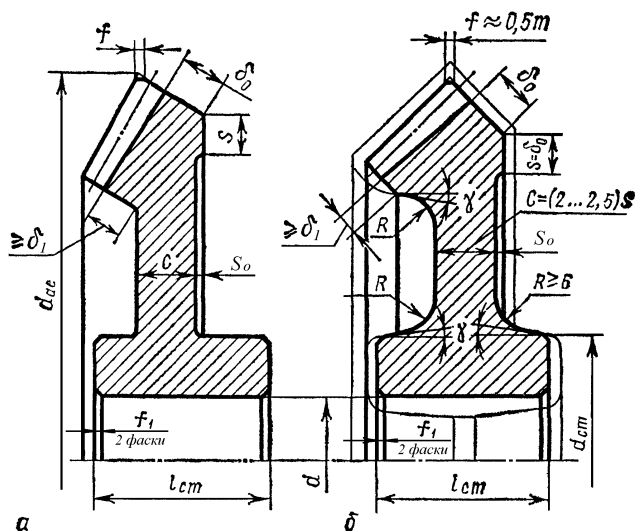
Конструктивная форма конических зубчатых колёс
